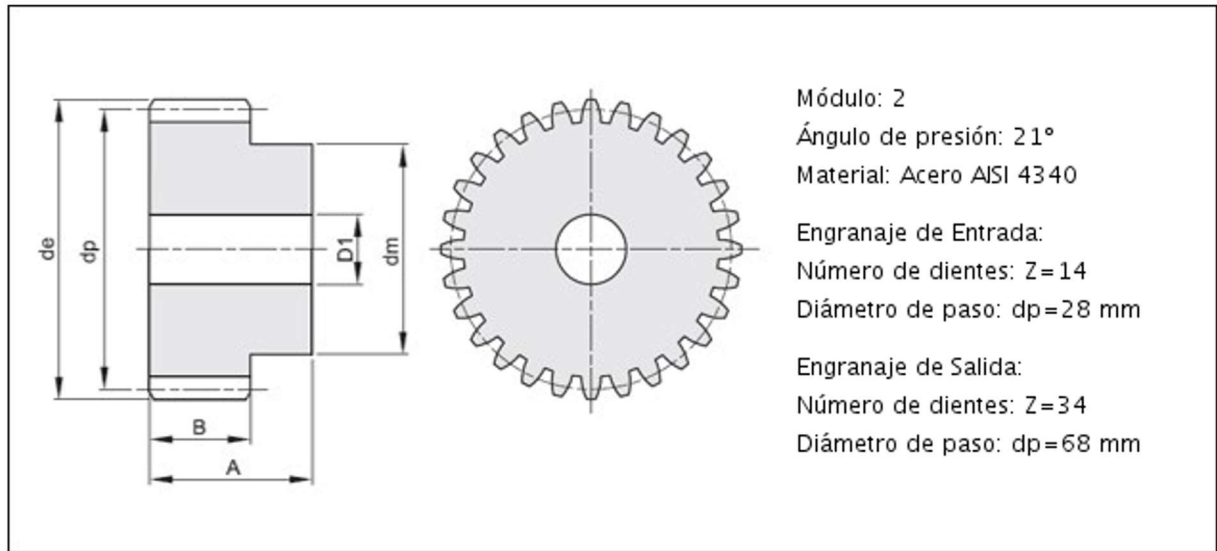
Engranajes de la etapa 1 de la caja reductora 2
